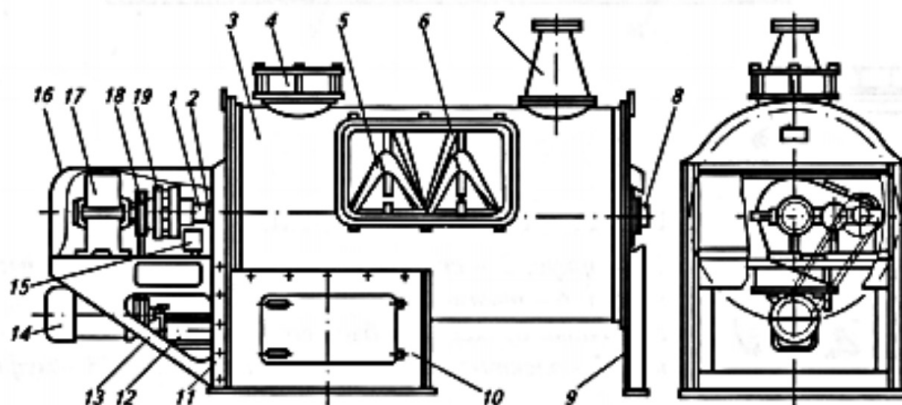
Горизонтальный смеситель А9-ДСГ-0,5: 1 – вал; 2, 8 – корпуса подшипников; 3 – корпус; 4, 7 – патрубки; 5, 6 – спиральные лопасти; 9, 11 – стойки; 10 – подсмесительный бункер; 12 – пневмоцилиндр; 13 – рама; 14 – электродвигатель; 15 – воздухораспределитель; 16 – ограждение; 17 – редуктор; 18 – клиноременная передача; 19 – муфта
